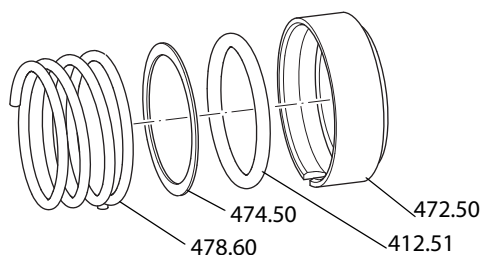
Finalizar el montaje en el árbol, aplicación E
